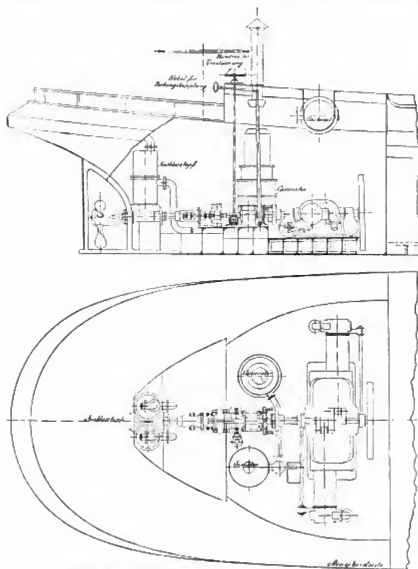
Flussschiff mit Achsengenerator u. 40 HP vis à vis - Motor.
